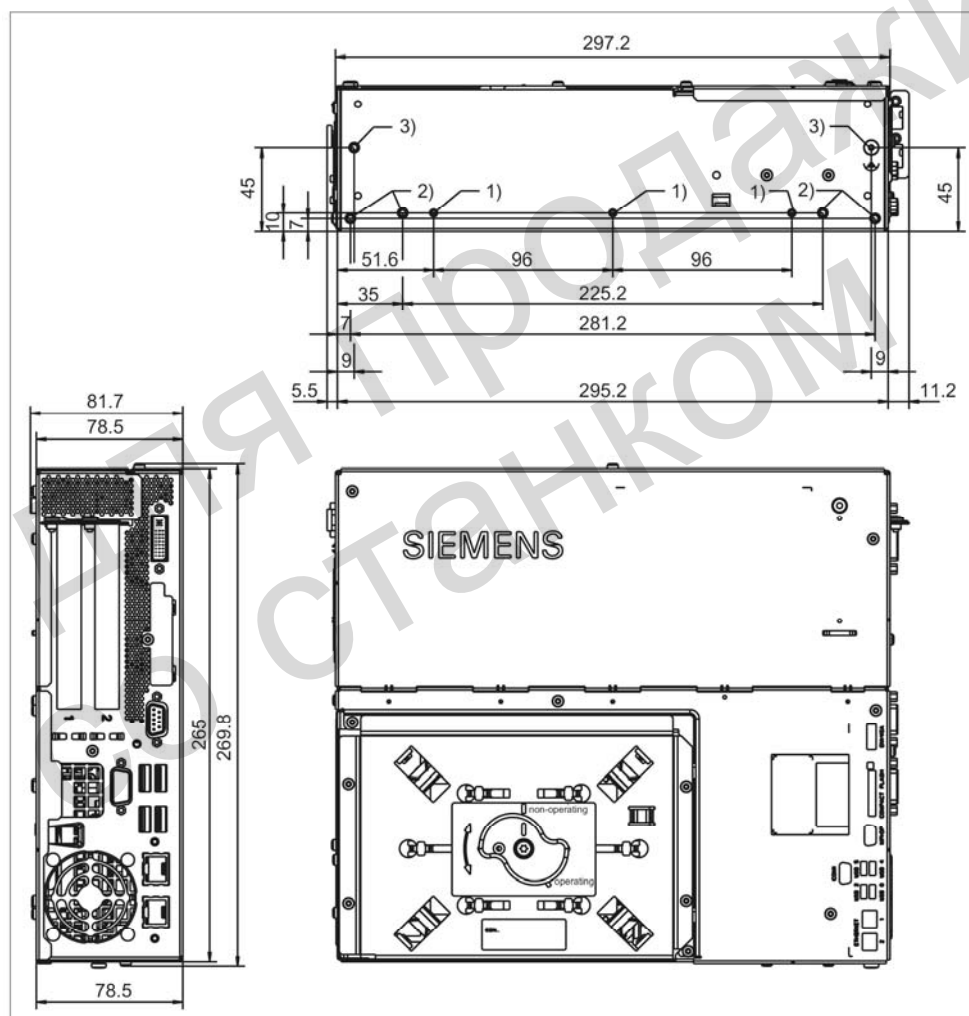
PCU 50.3 габаритный чертеж для монтажа без разгрузки от натяжения ЕТН
